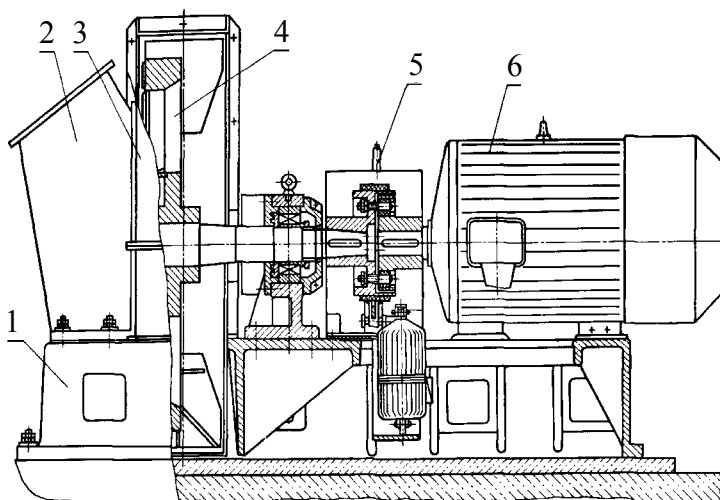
Общий вид дисковой рубительной машины МР2-20 [22]:
